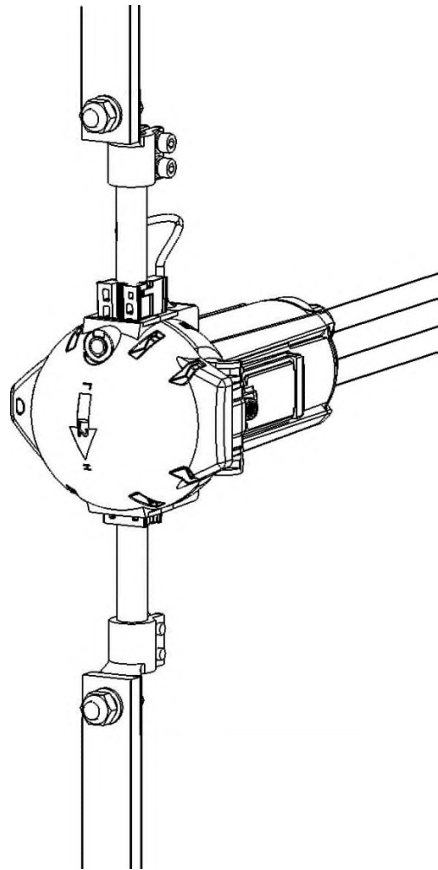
Установленный блок соединительный на шине распределительного устройства.
